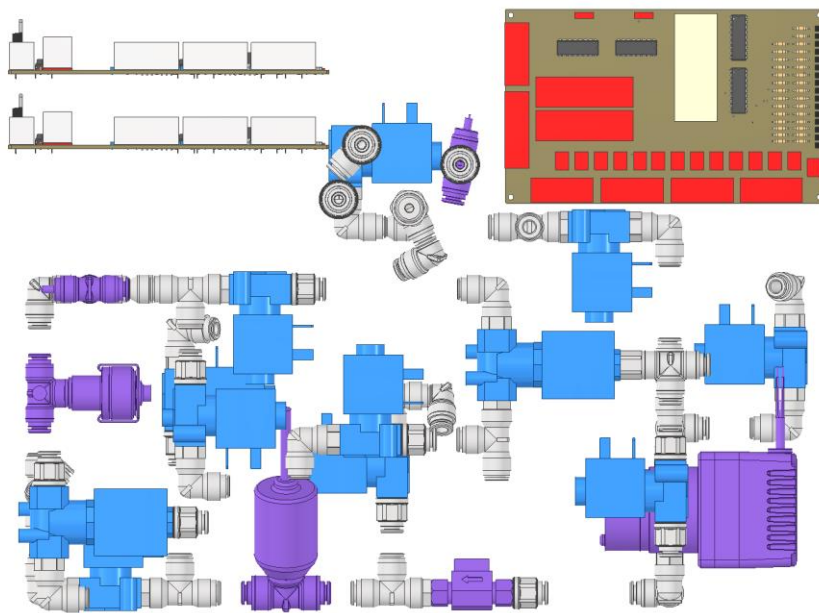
Konzept 2 der Komponenten im Unterbau; Draufsicht
